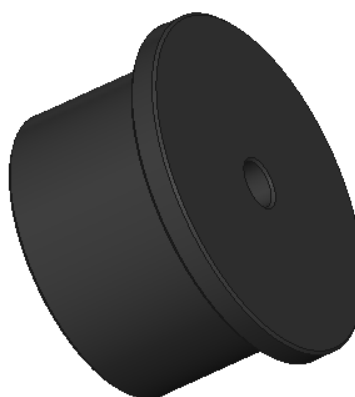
Colocação das rodas de nylon na estrutura metálica.
